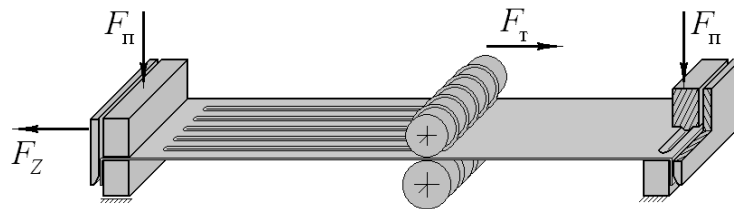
Способ изготовления профилей с плоскими концевыми участками
